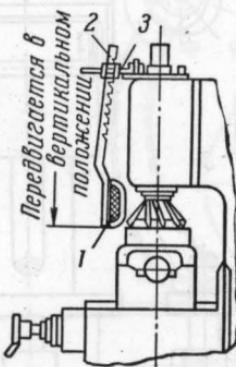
Предохранительное устройство для защиты от отлетающей стружки на вертикально-фрезерных станках.
